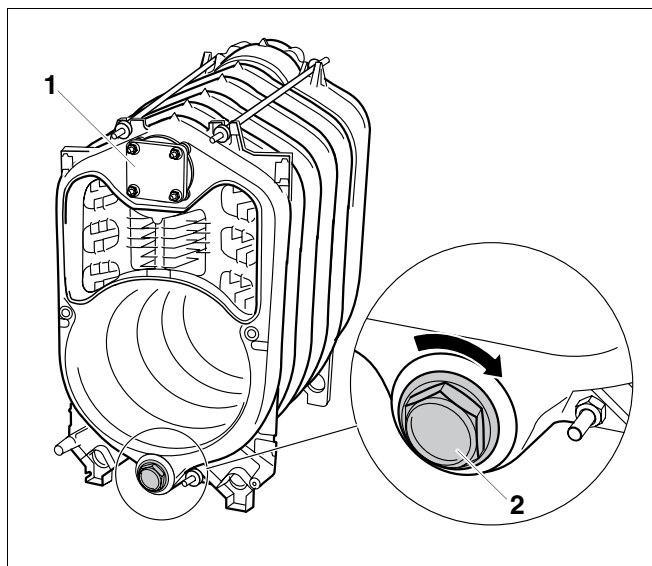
Închiderea butucilor cazanului pe elementul frontal
